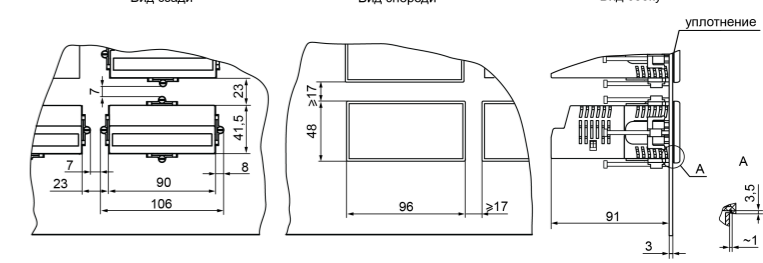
Монтаж прибора щитового крепления Щ2
